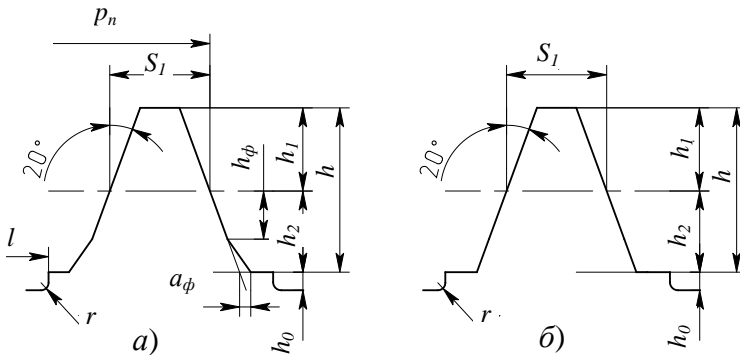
Розміри профілю зубів фрези для коліс:
